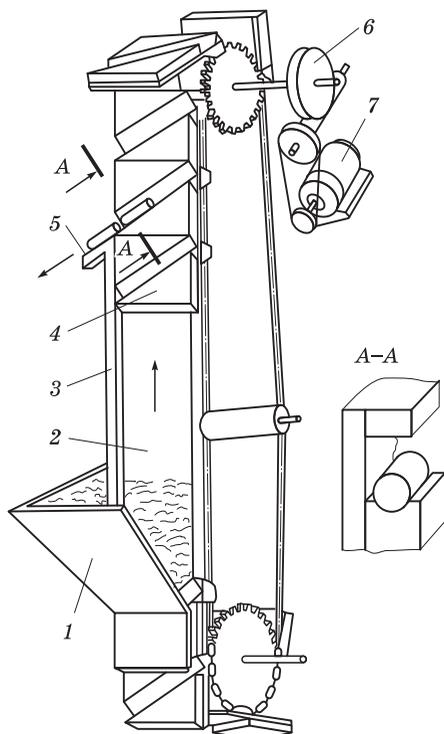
Схема скребкового загрузочного устройства элеваторного типа
